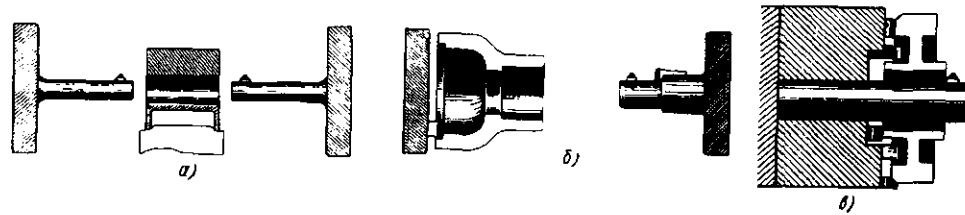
Схемы растачивания отверстий с установкой и закреплением детали на столе станка: а – на горизонтальном двустороннем станке; б – на горизонтальном одностороннем станке (последовательное растачивание двух отверстий); в – на горизонтальных одно- и двусторонних станках с применением многолезвовой наладки
